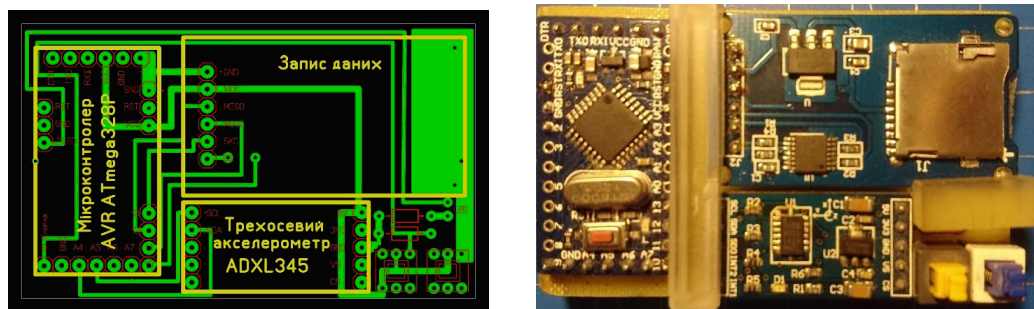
Принципова схема та загальний вигляд пристрою для вимірювання прискорень
